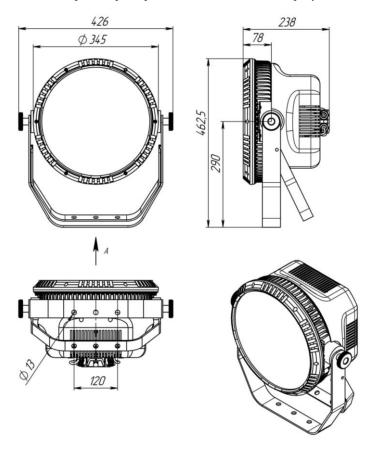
Габаритные размеры светильника «L-banner 600 Sport»
